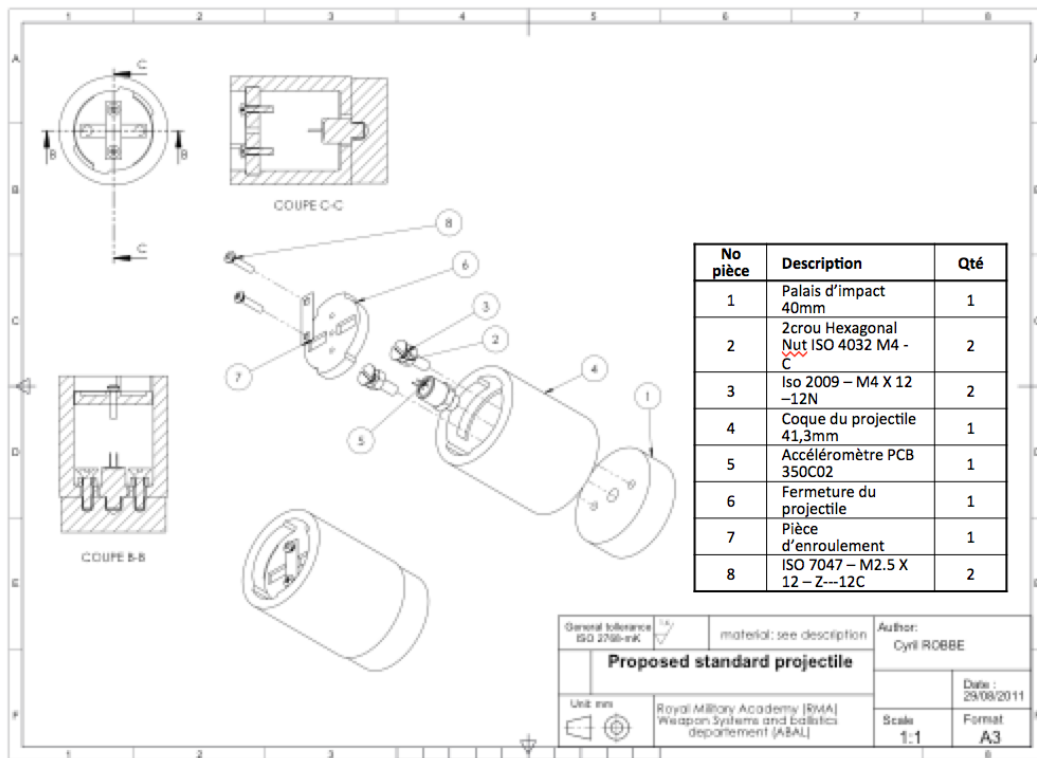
Le plan d'assemblage de la version finale du projectile instrumenté.
